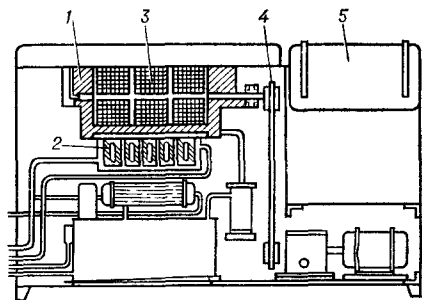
Схема механизированной ультразвуковой ванны: 1 — корпус ванны; 2 — преобразователи; 3 — загрузочные сетчатые барабаны; 4 — привод; 5 — пульт управления.
